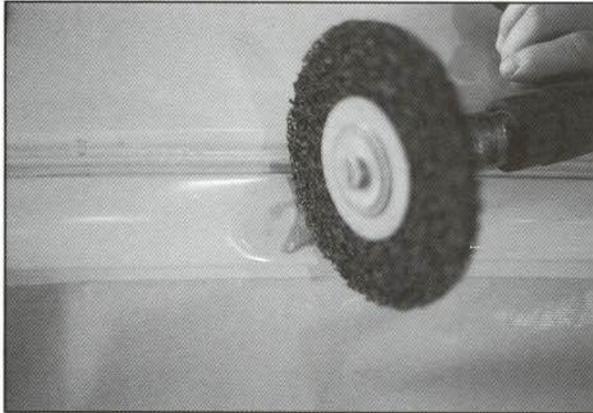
Pequeño golpe en estribo bajo puerta.
